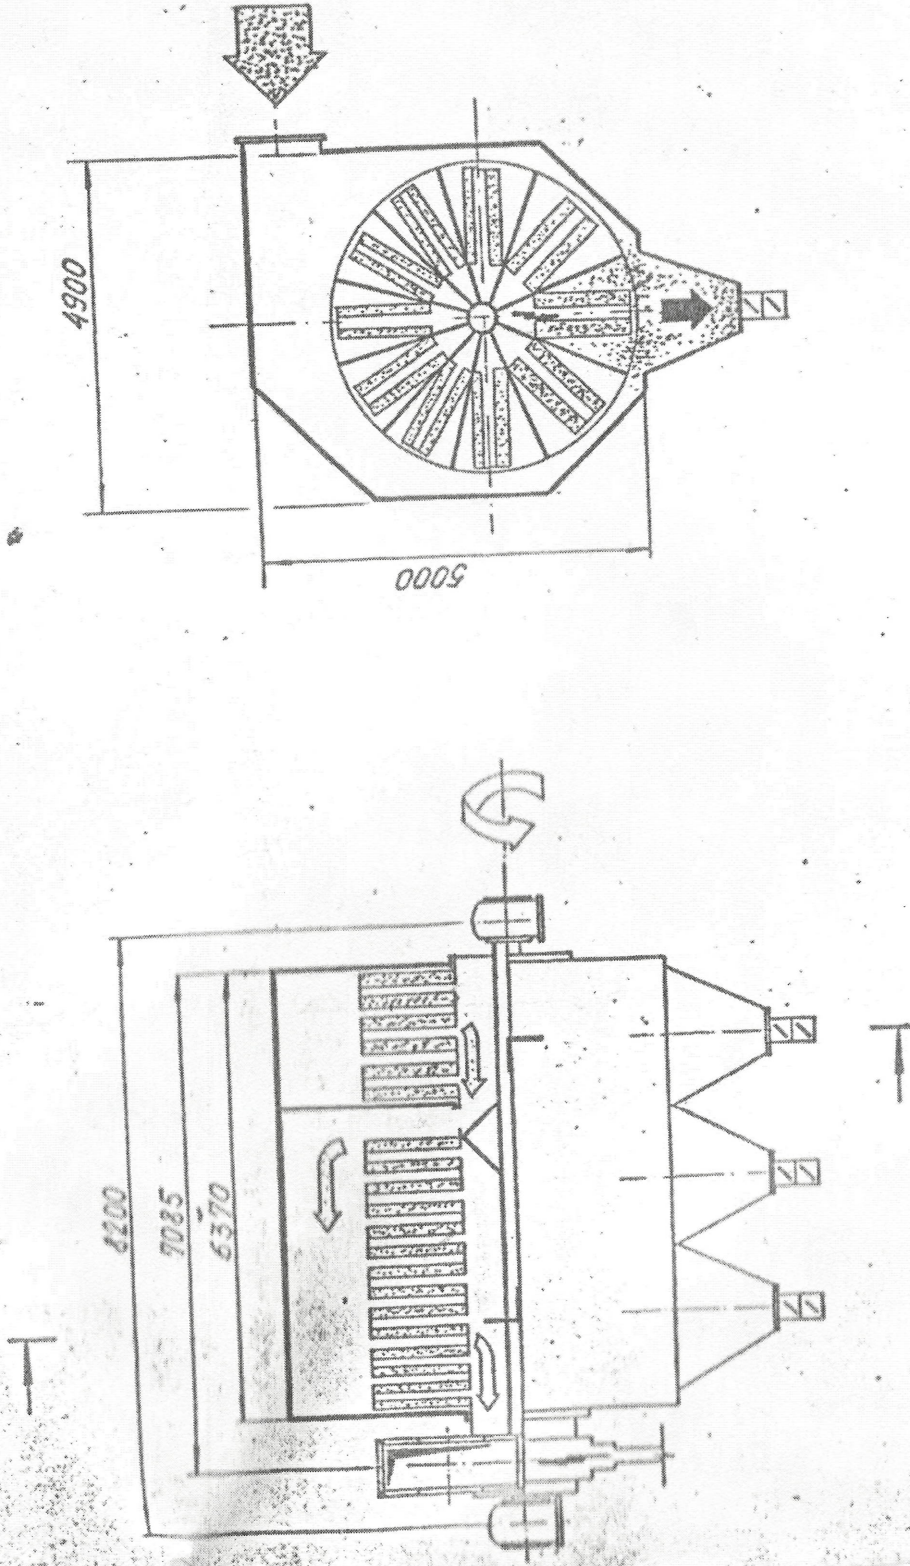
габаритный чертёж фильтра ФРЗВ-75/200.
